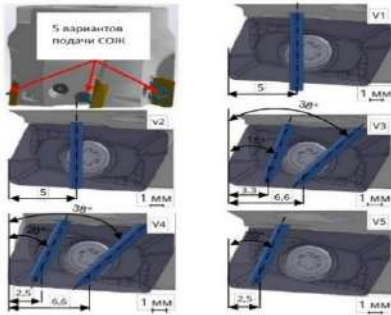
Вариант фрезерного инструмента и охлаждающего сопла
